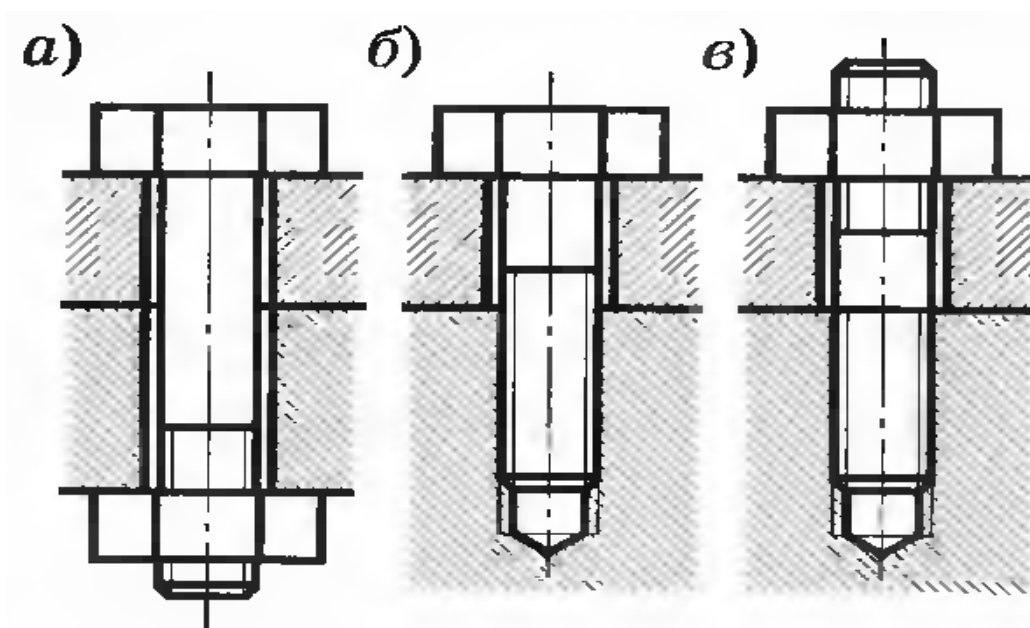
Виды резьбовых соединений: а — болтовое; б — винтовое; в — шпильчное
